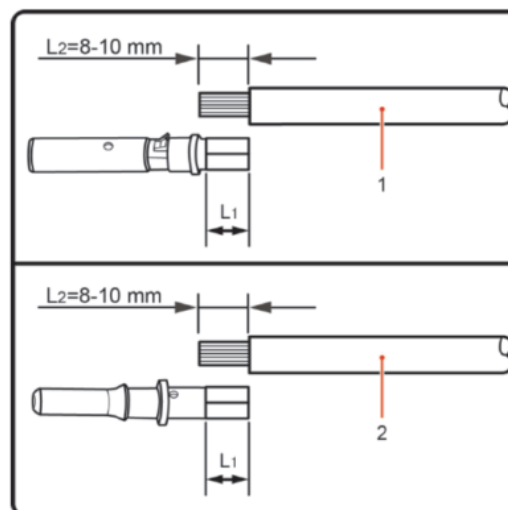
позитивний (1) і негативний (2) роз'єми MC4
